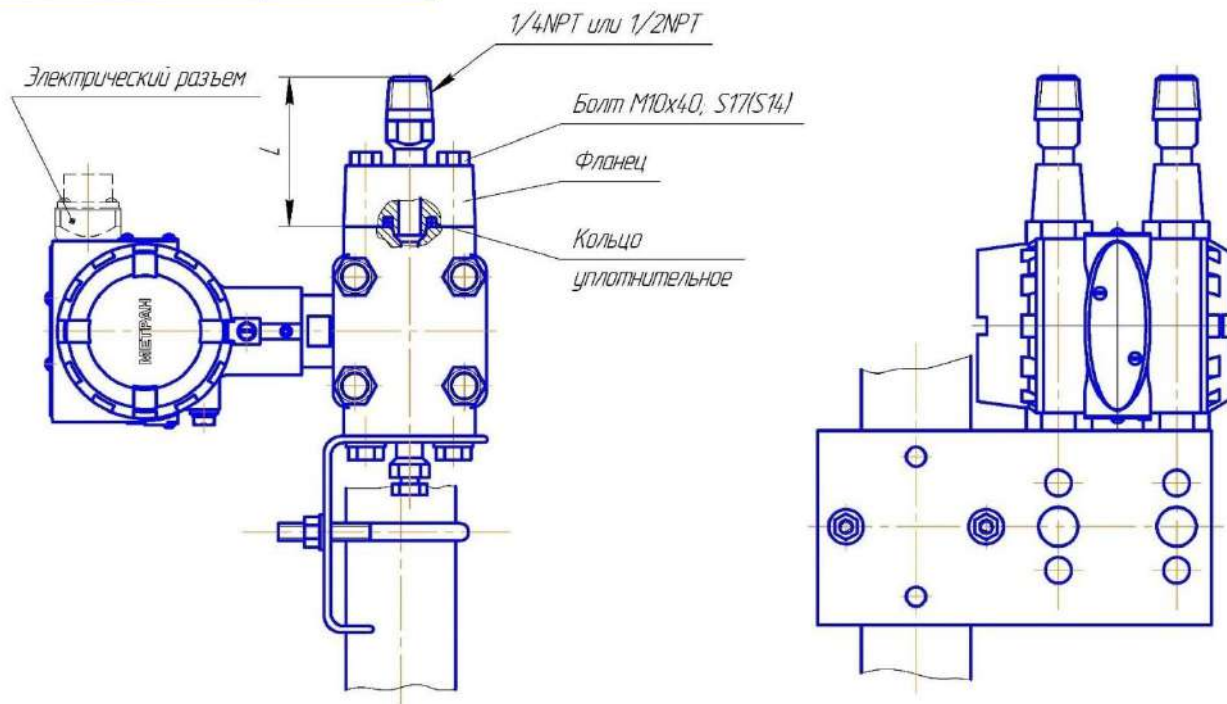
Датчики модели 150CD с установленными монтажными фланцами с резьбовым отверстием K1/4" (код D1), или K1/2" (код D2), или 1/4NPT (код D3), или 1/2NPT (код D4) и монтажным кронштейном для установки на двухдюймовой трубе (код B1 или B4)
